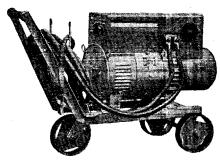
Schweißumformer Type QGS 41w mit Fahrgestell
